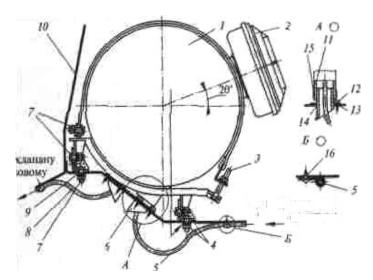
Монтаж баллона СНГ в багажнике: 1 -баллон; 2 -вентиляционный корпус; 3 -болт, стягивающий хомут; 4 и 7 -крепление ложемента к полу багажника; 5 -заправочная трубка; 6 -вентиляционные штуцеры; 8 -расходная трубка; 9 -отверстие в полу багажника; 10 -стенка багажника автомобиля; 11 -вентиляционный рукав; 12 и 16
